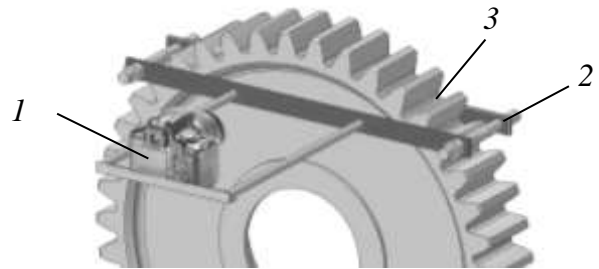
Схема отримання цифрових зображень зубців зубчатих коліс запропонованим способом: 1 – цифрова фотокамера; 2 – штатив; 3 – зубчате колесо
